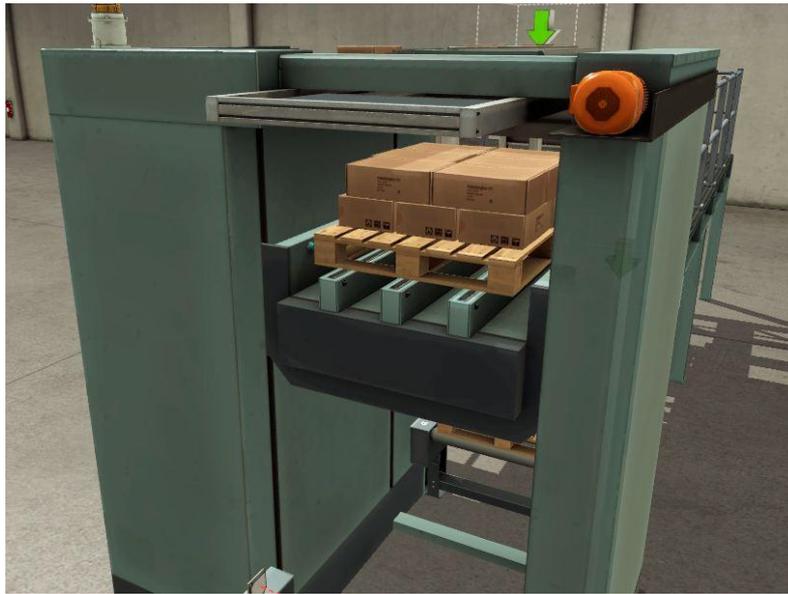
Cajas colocadas sobre el palet del almacén automático.
